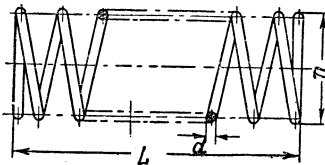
Пружина оттормаживающая тормозного цилиндра
